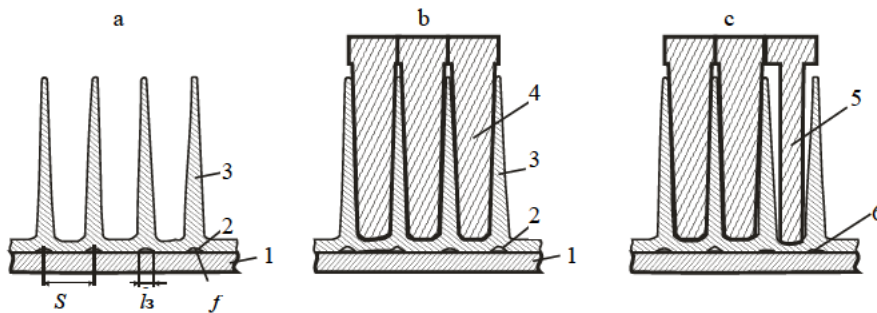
Схемы: а – зоны контакта биметаллической ребристой трубы; б – винтовой прокатки без обжатия; с – то же с дополнительным обжатием основания ребра;
